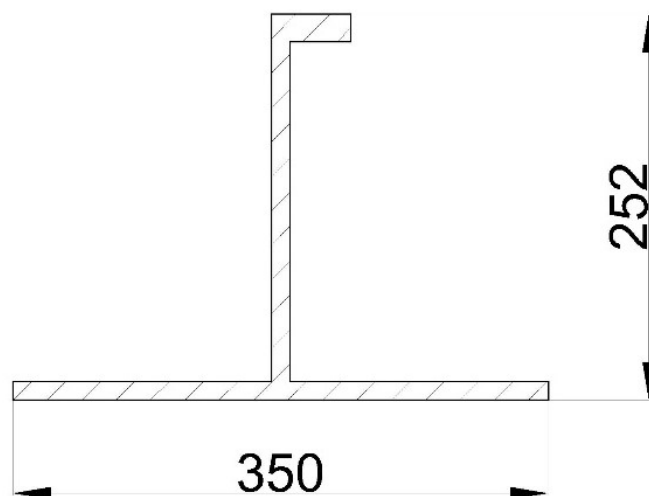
Переріз балки-шпангоута з приєднаним пояском для варіанта конструкції борту з подовженими проміжними шпангоутами
